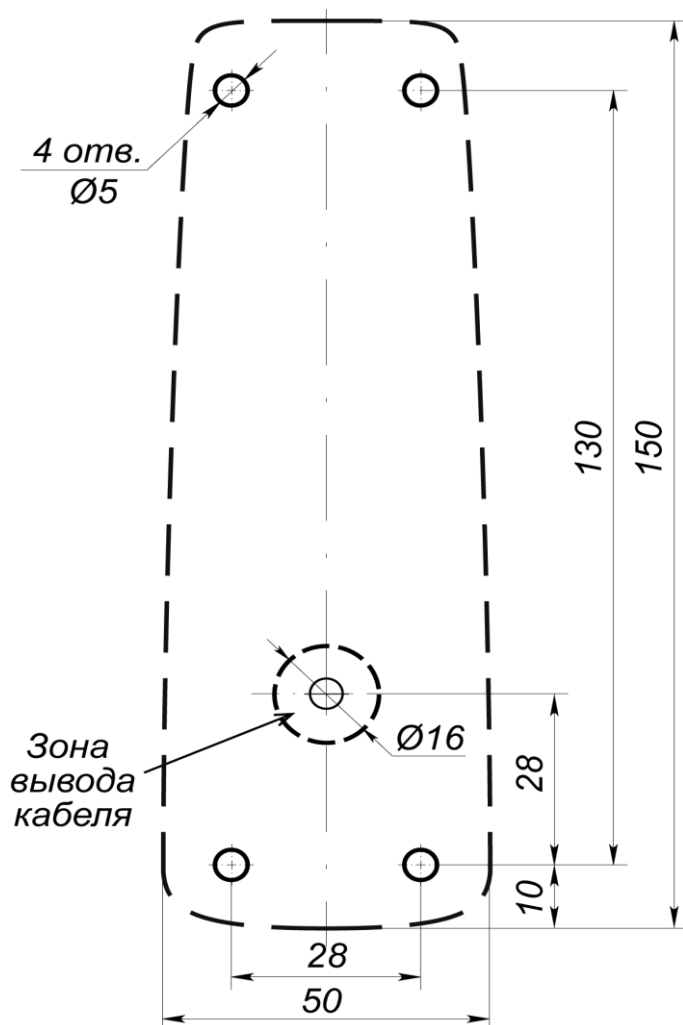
Разметка отверстий для установки контроллера (пунктиром показаны габариты корпуса контроллера)
